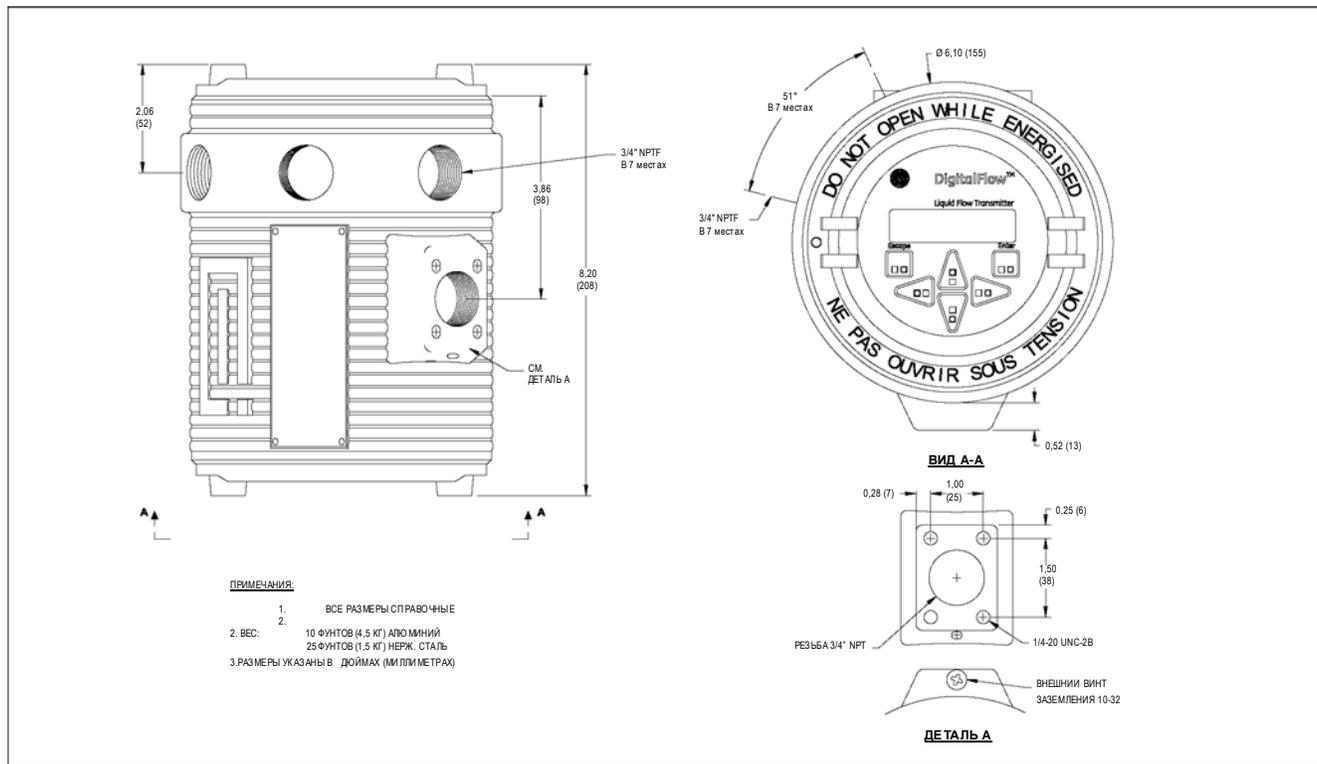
Эскиз и установка модели XGM868i (ссылочный № чертежа 712-1318)
